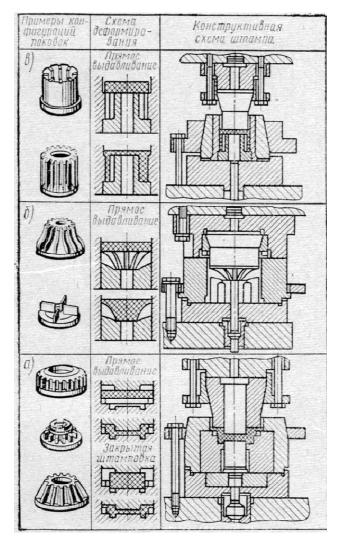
Схема деформирования и конструкции штампов для штамповки поковок с продольными и торцевыми ребрами на высокоскоростных молотах: а — поковки типа шестерен с оформлением зубчатого венца; б — поковки с наружными ребрами; в — поковки с глухой полостью и внутренними и наружными ребрами
